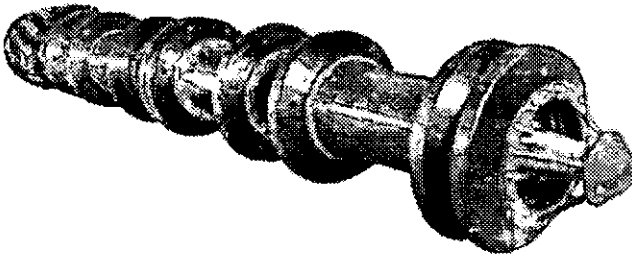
Herramienta de inspección interna ultrasónica
